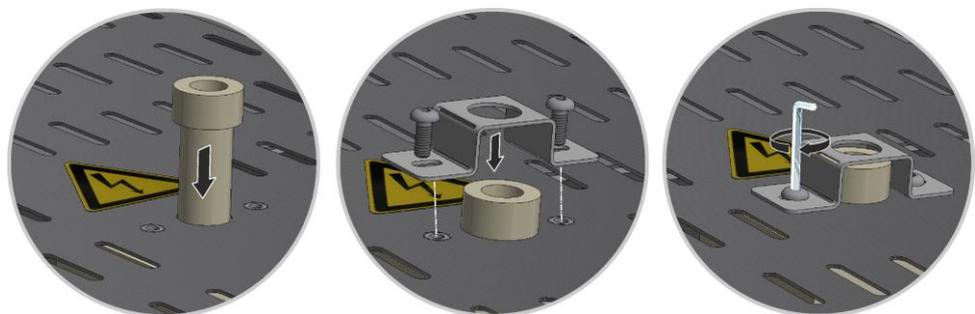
Montagem do tubo do ar de exaustão (semelhante à figura)
